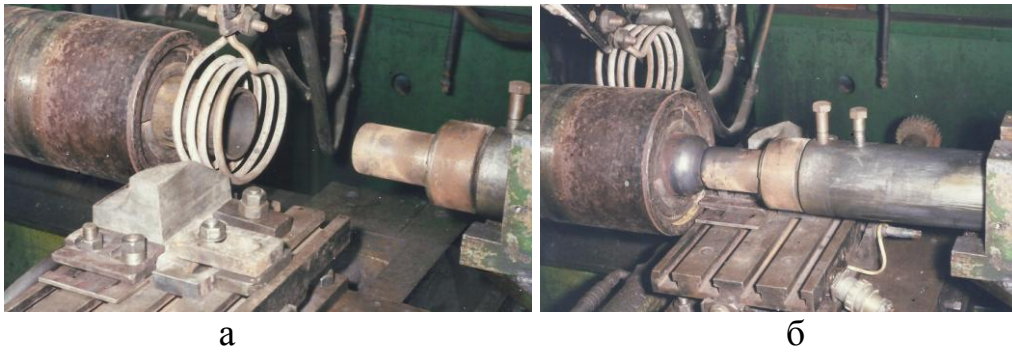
Індукційне нагрівання трубної заготовки перед обкочуванням (а) та підсадка сферичного днища (б)
